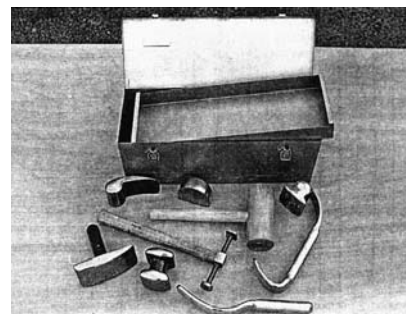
Набор инструментов и приспособлений для правки кузовных деталей
